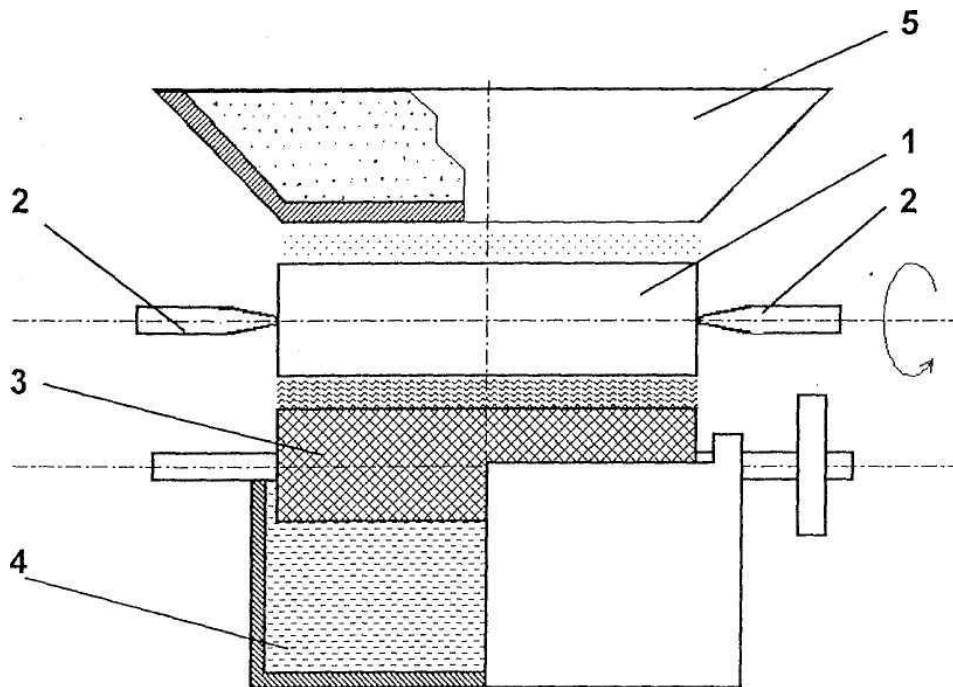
Принципова схема нанесення шлікерної обмазки на відновлювану деталь: 1 – відновлювальна деталь; 2 – центра; 3 – обмазувальний вал; 4 – ванна з мастилом; 5 – бункер з порошком
